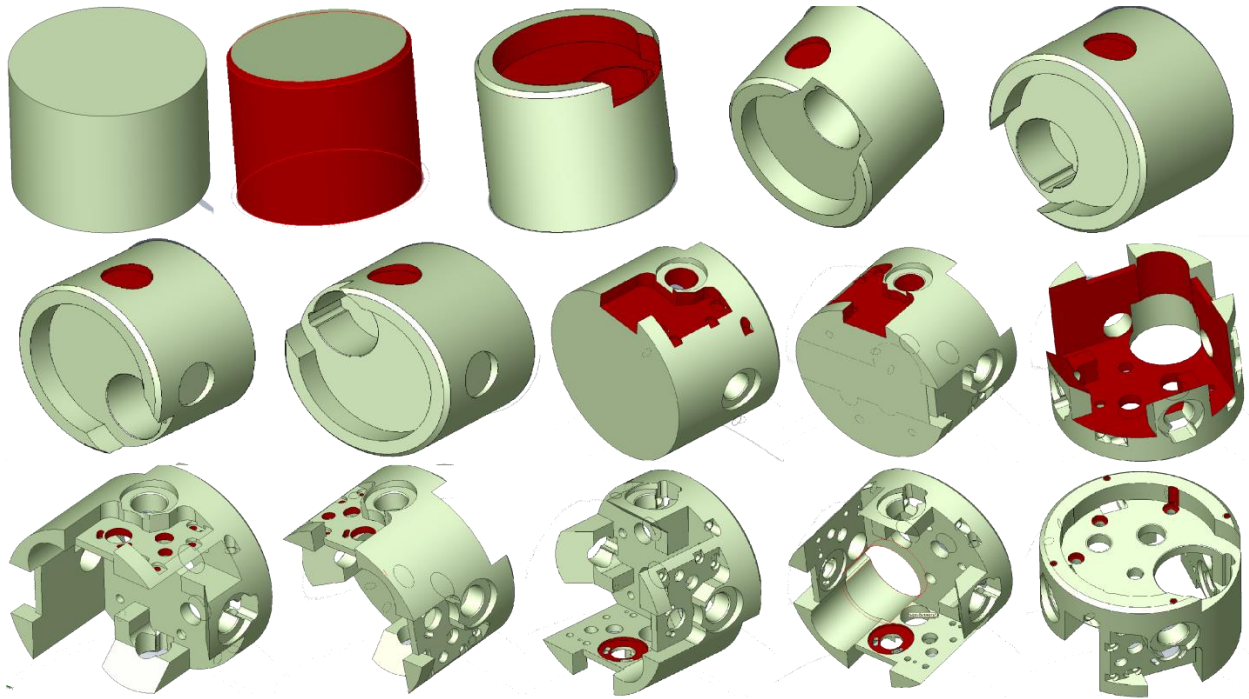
Комп'ютерна модель багатоопераційної обробки деталі
